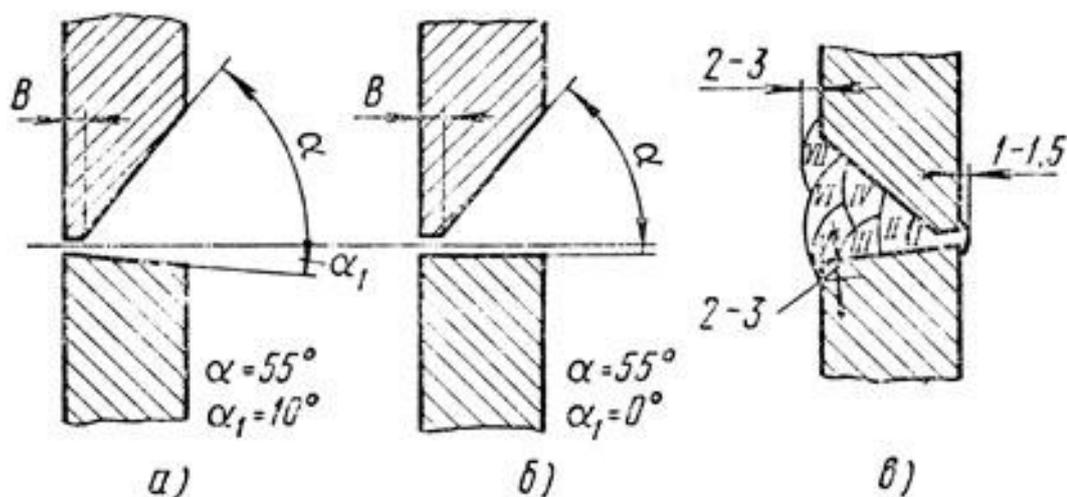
Схема разделки кромок горизонтальных сварных соединений ответственных (а) и неответственных (б) трубопроводов и сварки (в).
